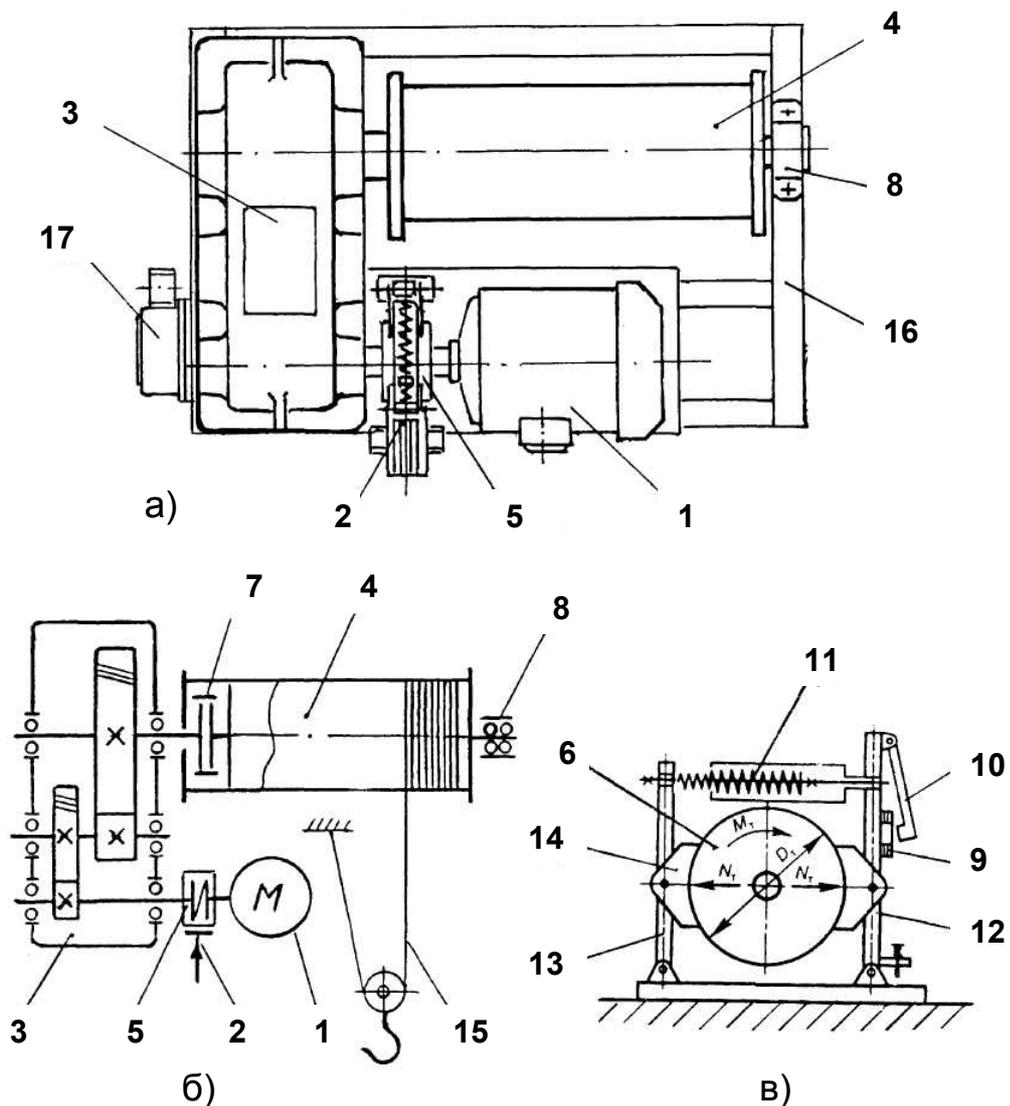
Лебёдка электрореверсивная : а) общий вид; б) кинематическая схема лебёдки; в) схема колодочного тормоза
